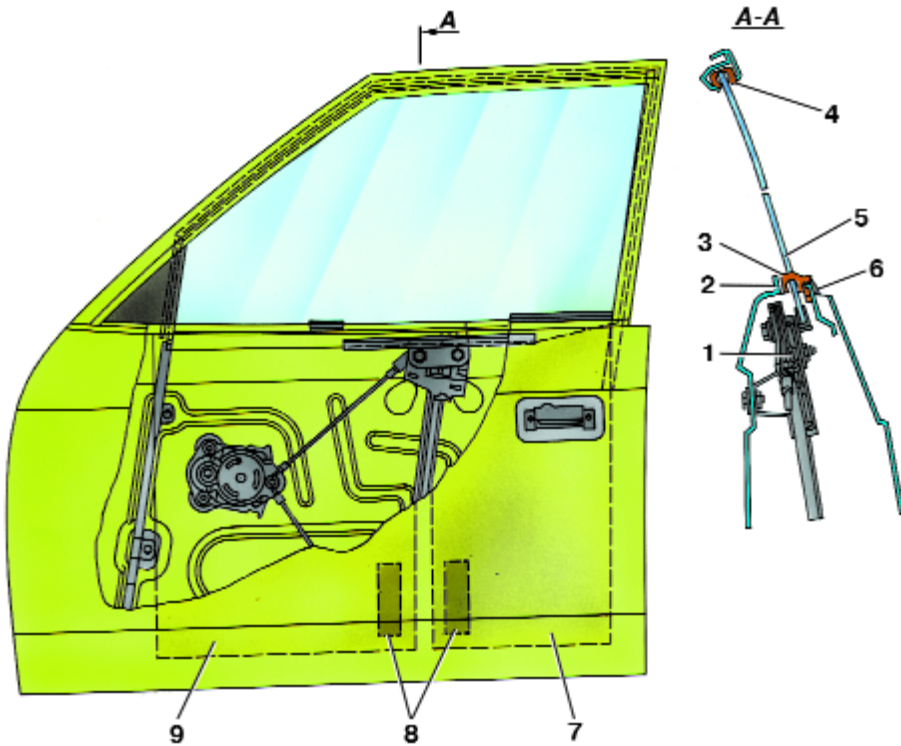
Установка опускного стекла передней двери: 1 – болт крепления опускного стекла; 2 – держатель уплотнителя; 3 – уплотнитель; 4 – желобок; 5 – стекло; 6 – накладка; 7 – клапан влагозащитный малый; 8 – липкая лента; 9 – клапан влагозащитный большой
